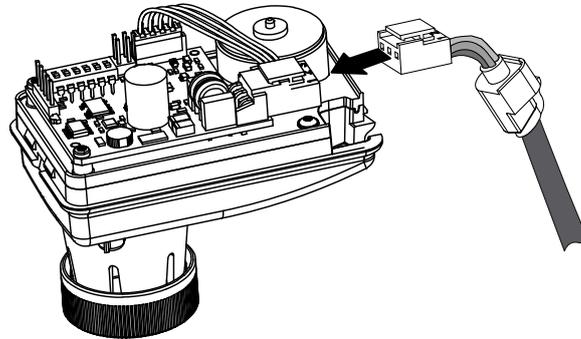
Steckverbinder in die Anschlussbuchse stecken
